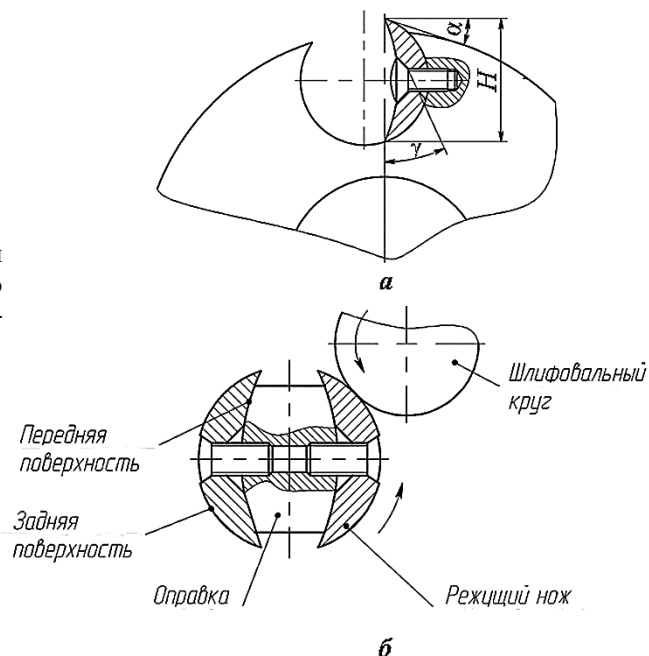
Узел крепления серпообразного режущего элемента (а) и схема заточки ножей по задней поверхности (б)
